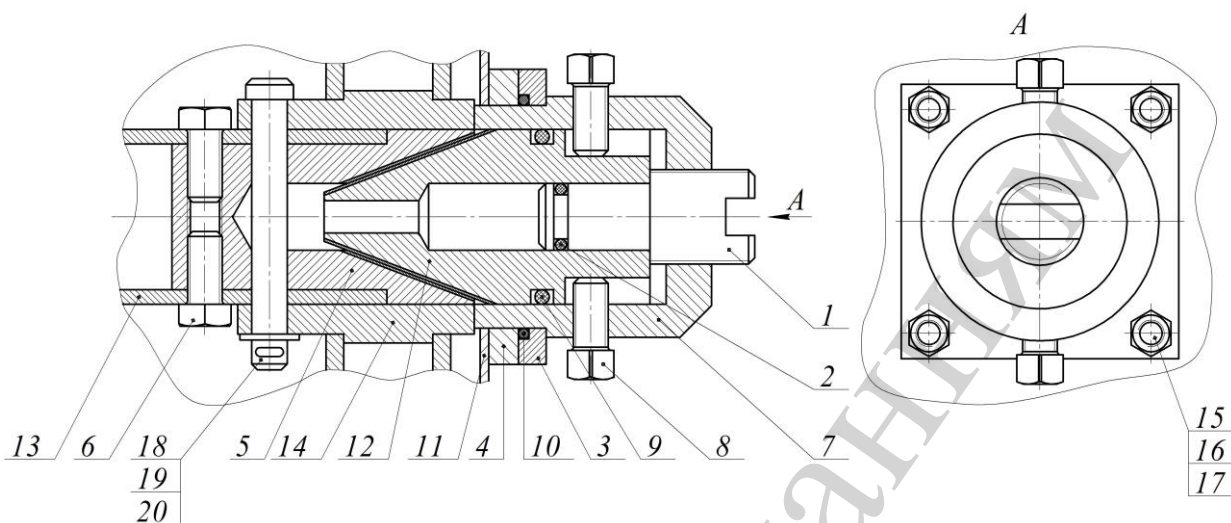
Опора ковзання: 1 – гвинт притискання; 2, 9, 10 – кільце ущільнююче; 3, 4 – фланець; 5 – вставка; 6 – гвинт; 7 – корпус; 8 – гвинт регулювання; 11 – стінка змішувача; 12 – цапфа; 13 – вал змішувача; 14 – колесо цівкове; 15 – шпилька; 16 – гайка; 17 – шайба; 18 – палець; 19 – шплінт; 20 – штифт
